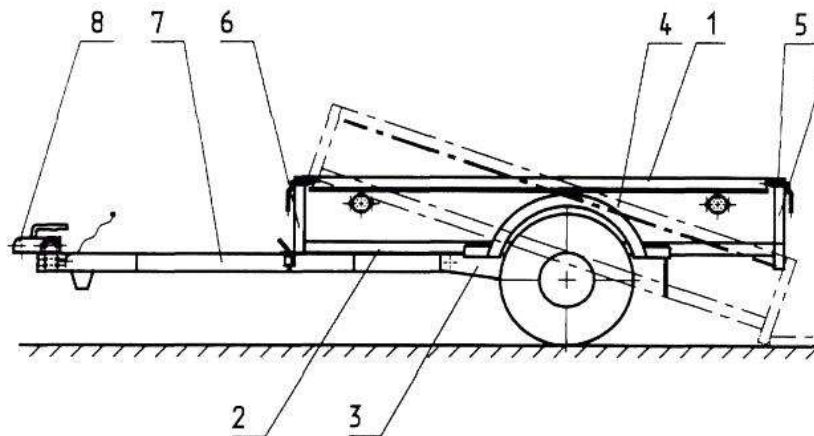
Схема причепа-самоскида з ручним перекиданням: 1 – кузов; 2 – дно; 3 – підвіска; 4 - колесо; 5 – замок; 6 – передній борт; 7 - дишло; 8 – зчіпний пристрій.
